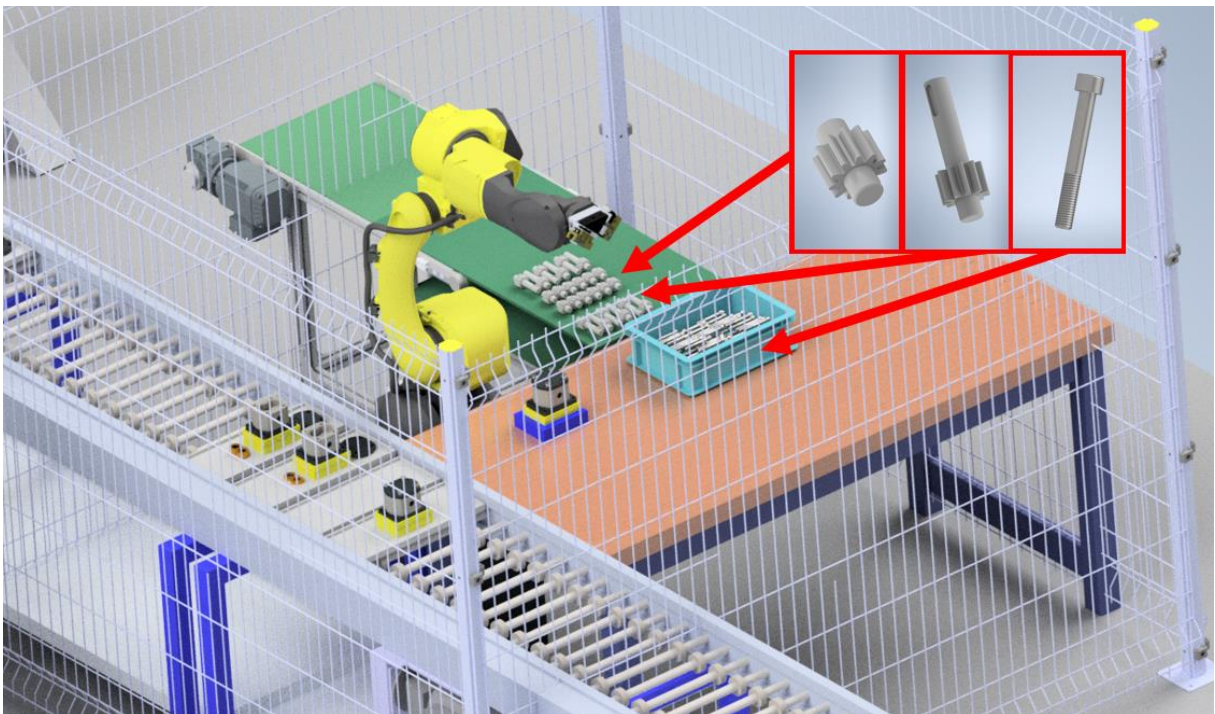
Varianta č. 1, stanoviště č. 2 a 4
